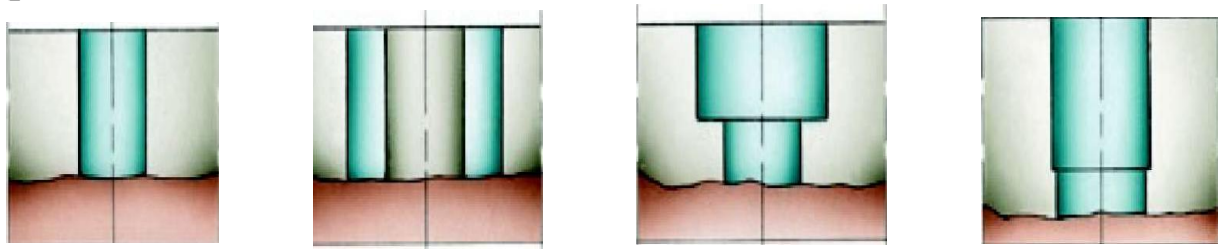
Обработка отверстий: а – сверление; б - трепанирующее сверление; в – растачивание; г – развертывание.
